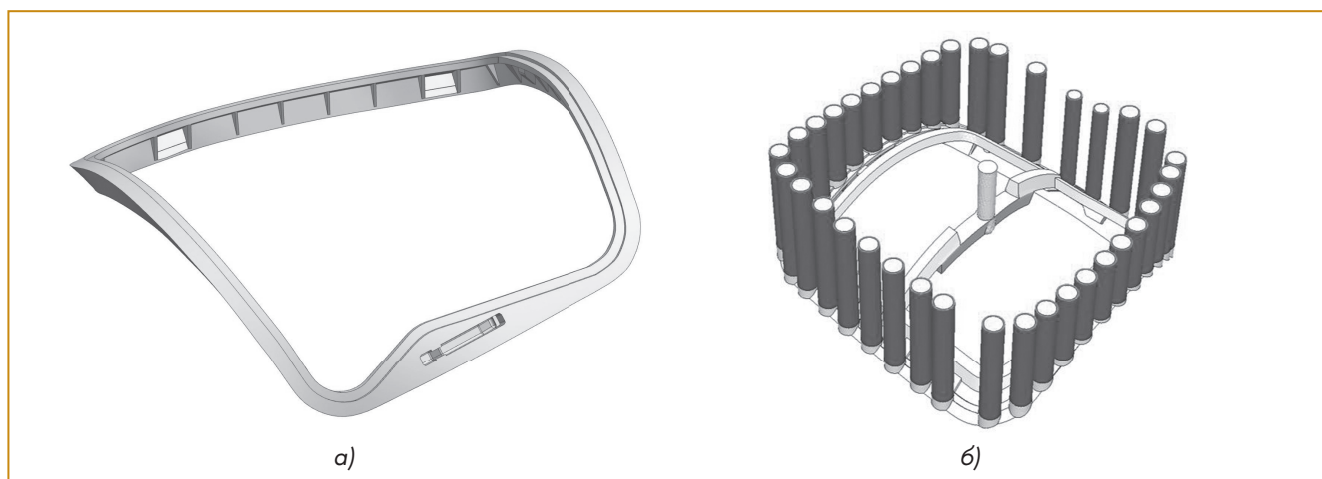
Конструкция ЛПС, применяемая на предприятии при изготовлении отливок типа «Рама»: а) 3D-модель отливки; б) 3D-модель литейного блока.
